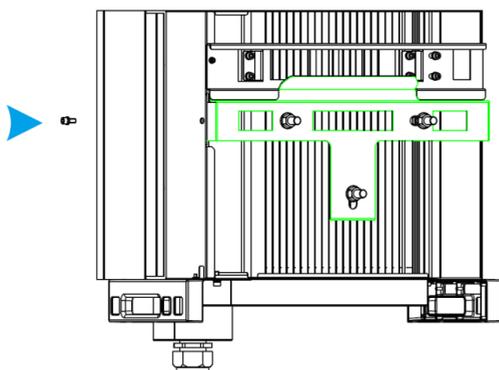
Montaggio della staffa sulla struttura di montaggio
